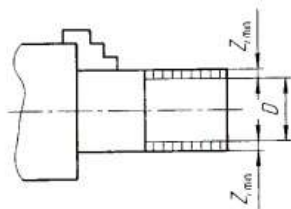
Ескіз обробки консольно закріпленої заготовки
